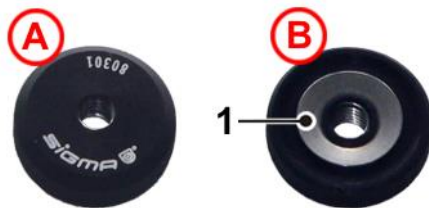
Écrou de fixation du rotor vu de dessus (A) et de dessous (B)
